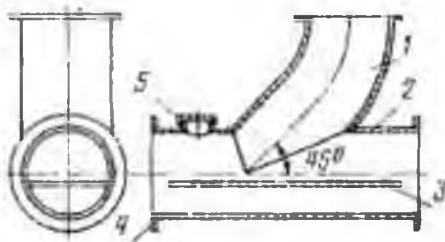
Приймач типу «трійник»: 1-приймальний патрубок; 2-труба; 3-перегородка; 4-фланець; 5-продувний патрубок
